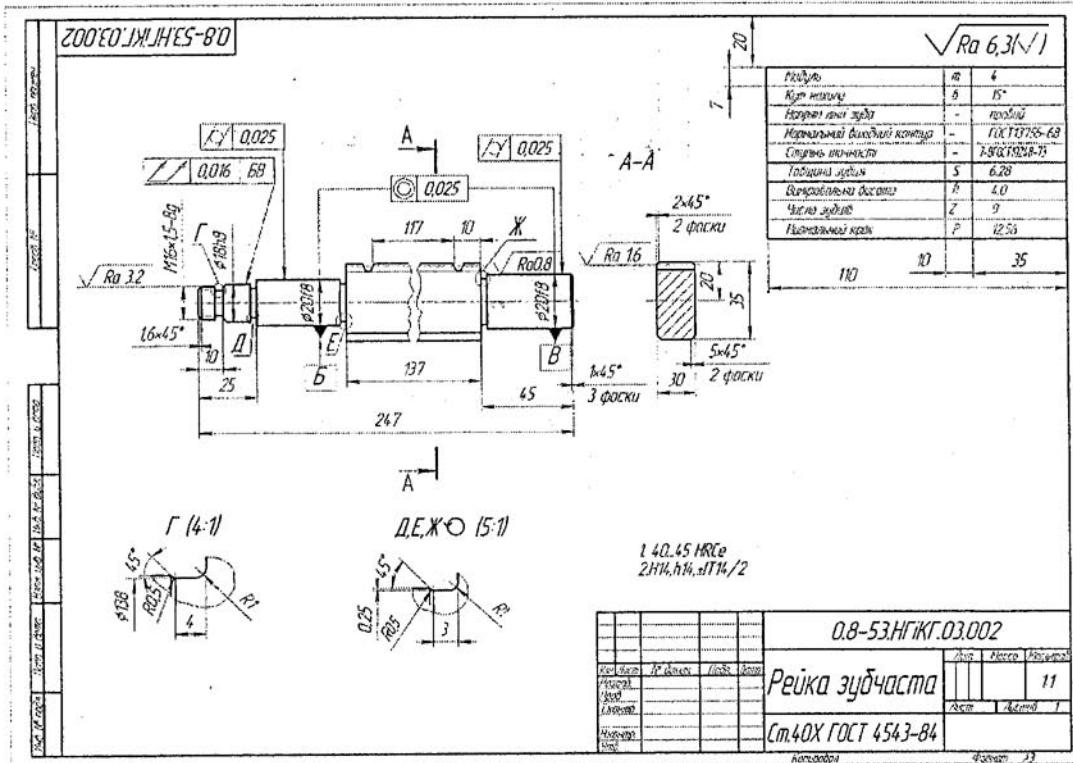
Робочий кресленик (working drawing) косозубої рейки
